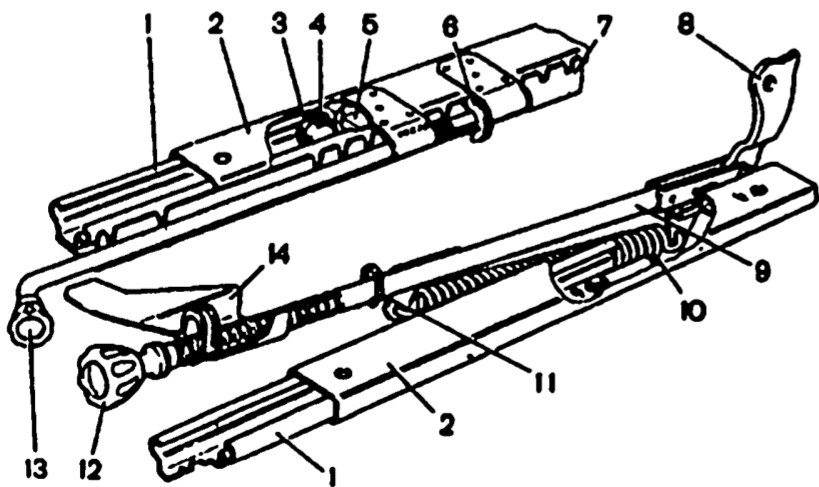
Механизмы регулировок переднего сиденья: 1 - направляющие салазок; 2 - ползуны салазок; 3 - ролик; 4 - резиновое кольцо ролика; 5 - ограничитель; 6 - защелка салазок; 7 - фиксатор внутренней направляющей салазок; 8 - усилитель спинки; 9 - тяга; 10 - пружина; 11 - шплинт; 12 - винтовая тяга с рукояткой механизма наклона спинки; 13 - рукоятка механизма передвижения салазок; 14 - кронштейн винтовой тяги
